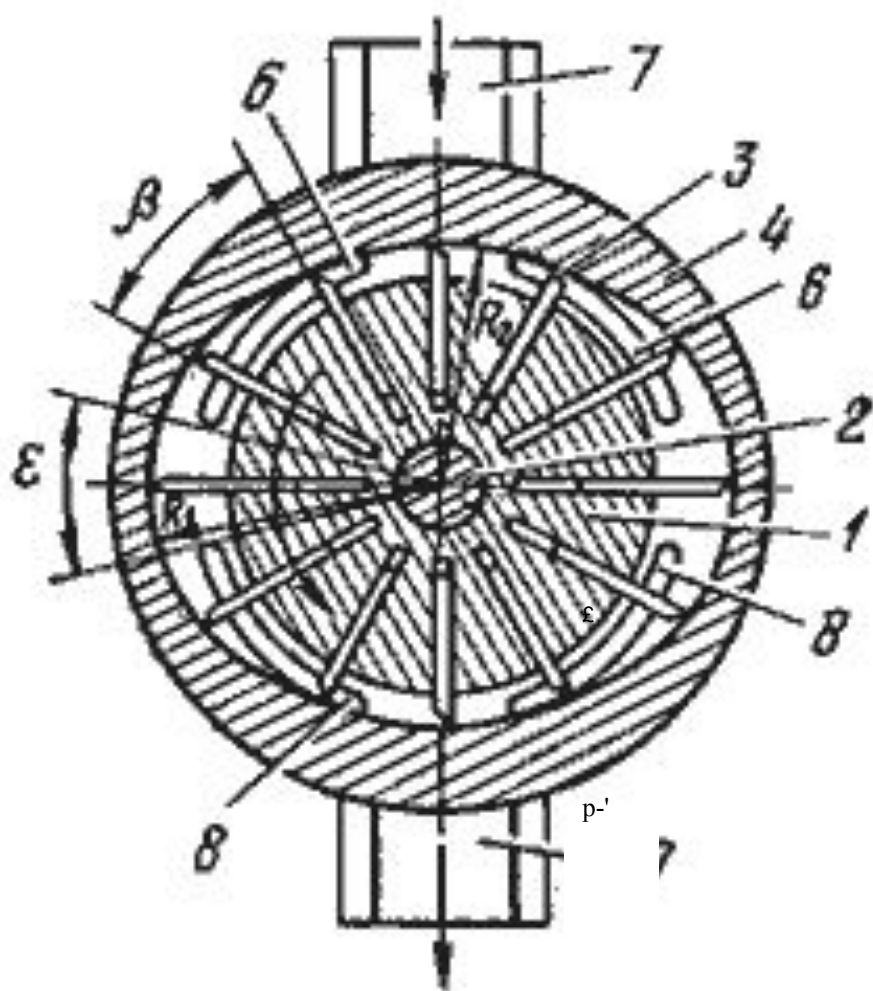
Схема пластинчатого насоса двойного действия: 1 - ротор; 2 - приводной вал; 3 - пластины; 4 - статор; 5 - распределительный диск; 6, 8 - окна; 7 - гидролиния всасывания; 9 - гидролиния нагнетания
